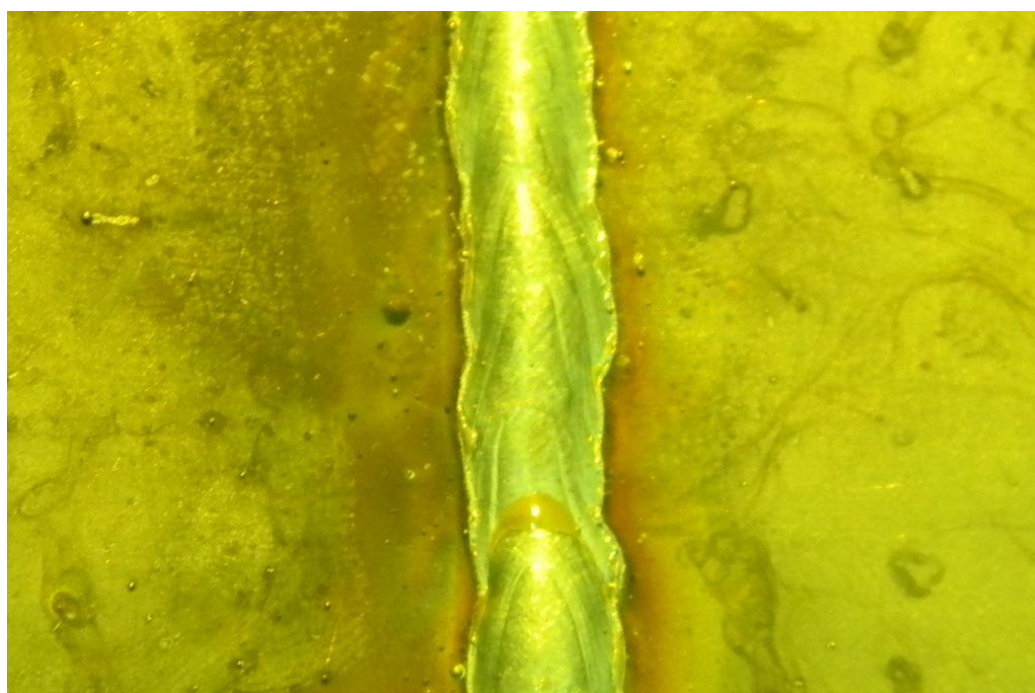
Образец после сварки подготовленный лазерной резкой
